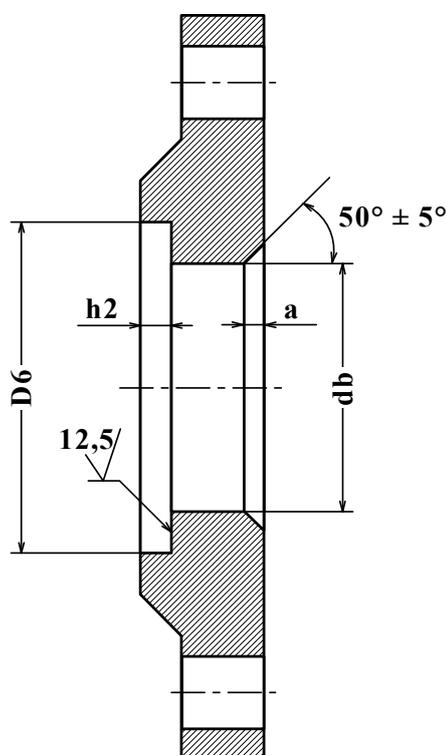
Сборно-сварная конструкция с фланцами
